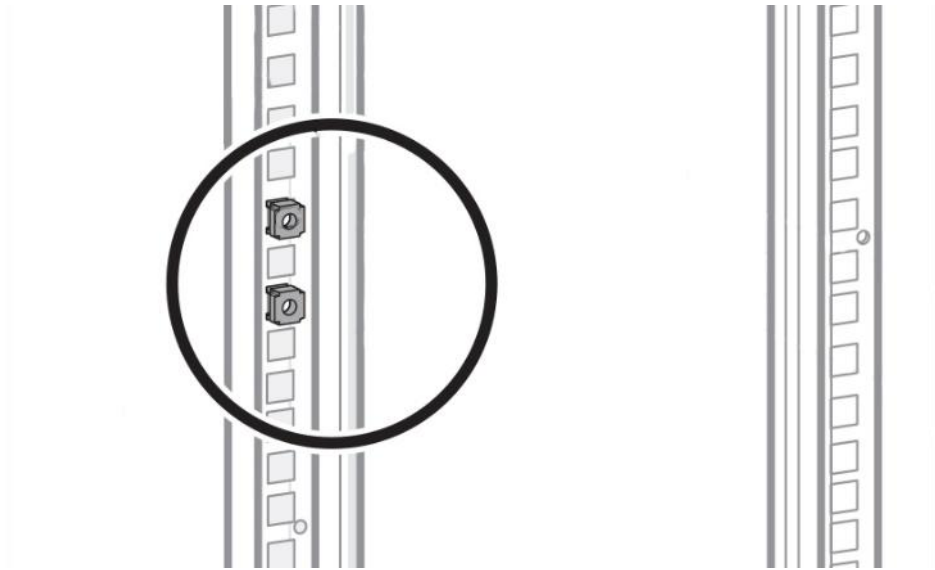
Установка клетевых стоечных гаек в монтажной стойке.
